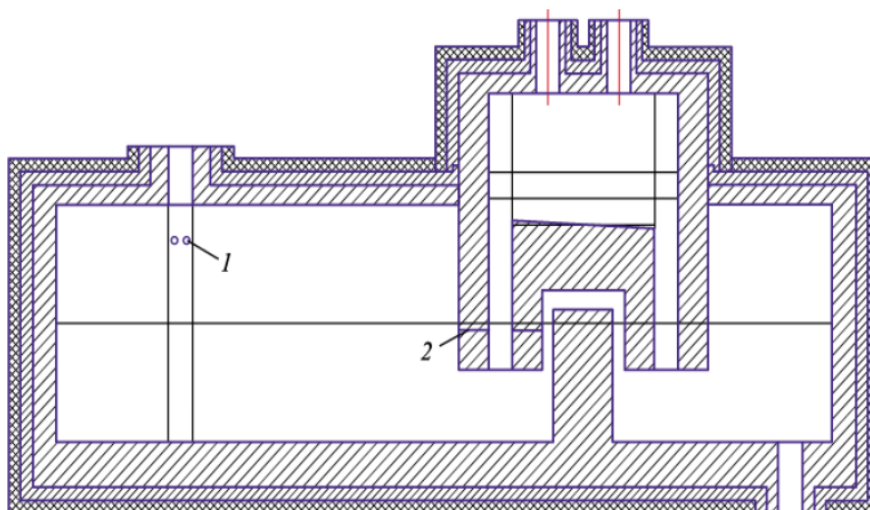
Эскизный чертеж реактора агрегата внепечной обработки расплава с вакуумным устройством:
